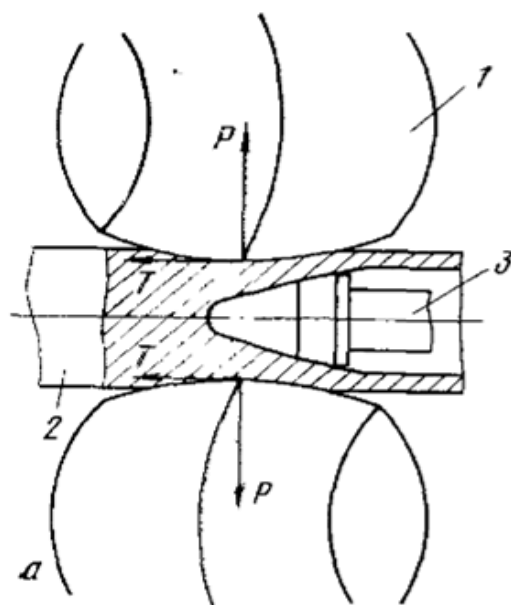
Схема прошивки заготовки в прошивном стане с бочковидными валками [12]:
